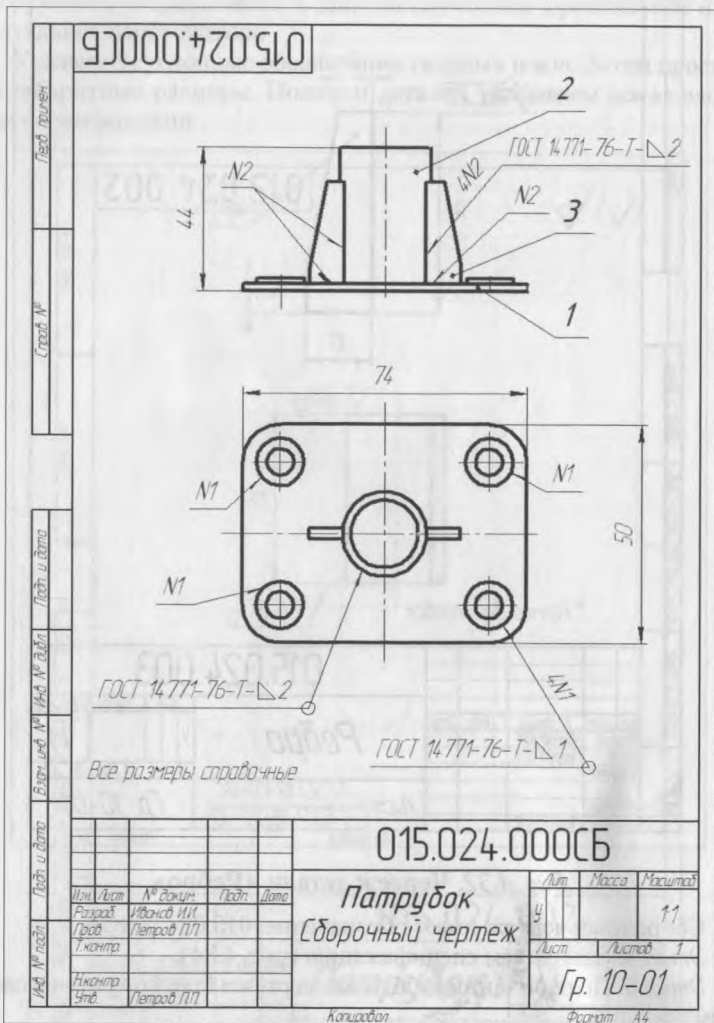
Сборочный чертеж изделия «Патрубок»
